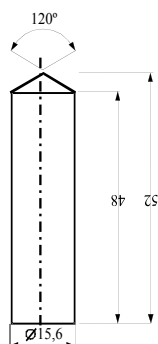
Êmbolo cilíndrico de bronze, dimensões em mm
